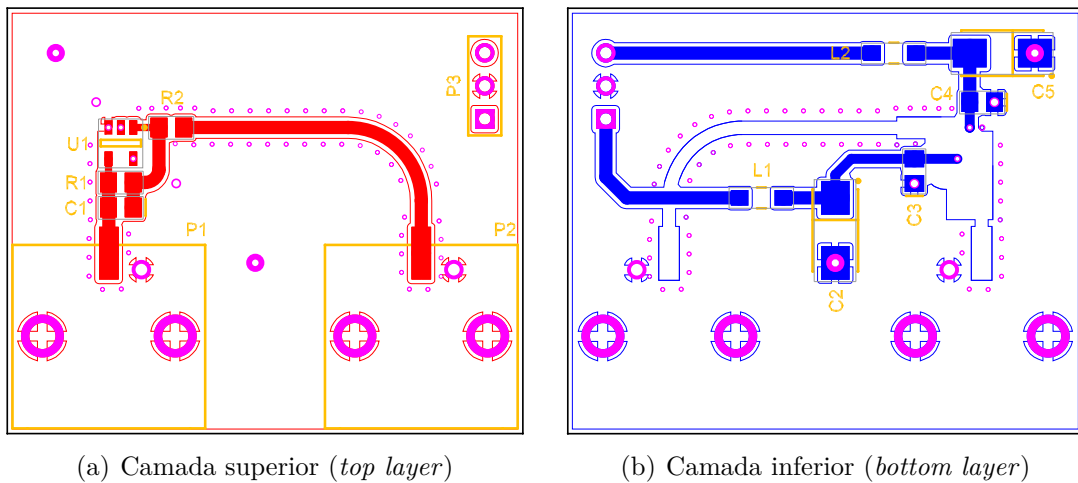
Placa de circuito impresso do condicionador de sinais. Fonte: Autor.
